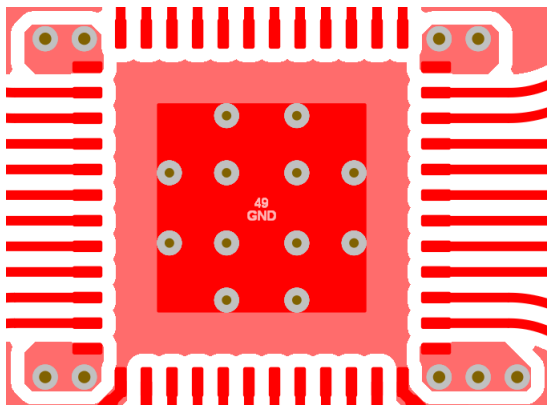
LMK1D2108L 的 PCB 布局示例，顶层
